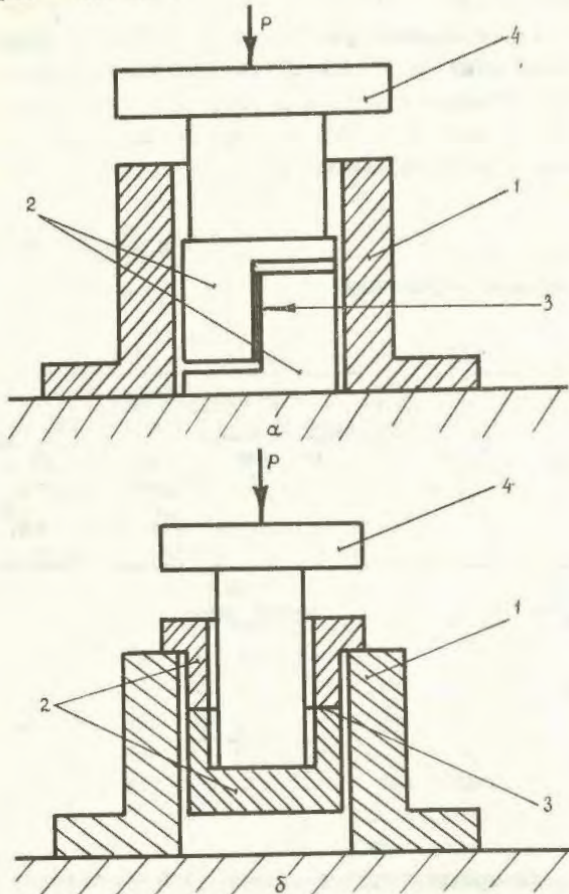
Схема статических испытаний клеевых соединений на сдвиг (а) и на отрыв (б): 1 - направляющая втулка; 2 - испытываемый образец; 3 - клеевой шов; 4 - нагружающий пуансон
